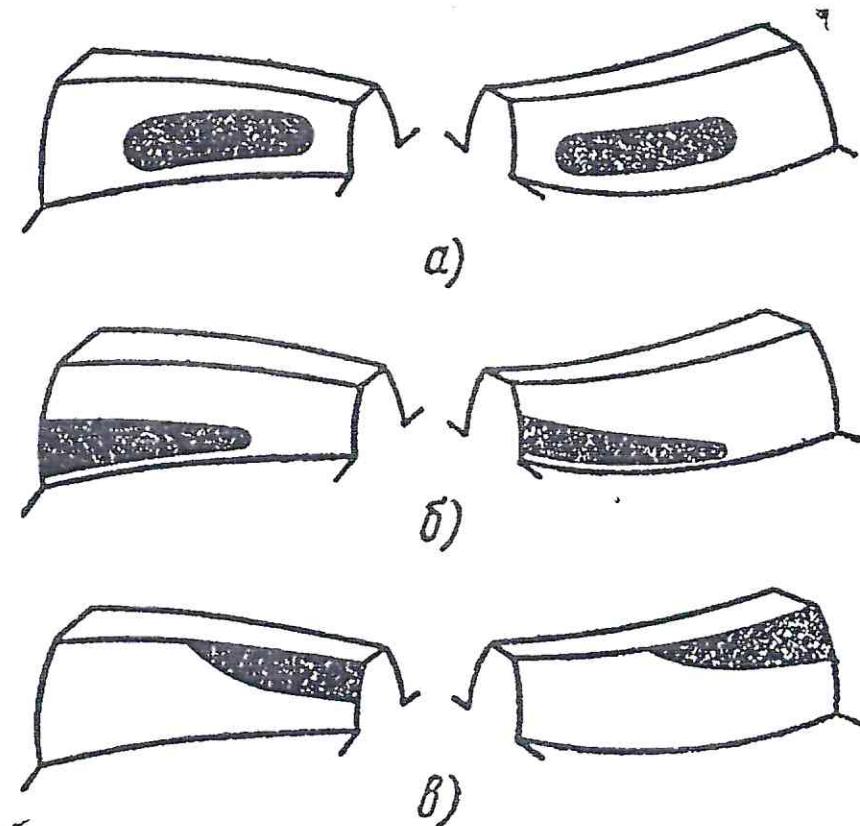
Расположение отпечатков ведомой шестерни
